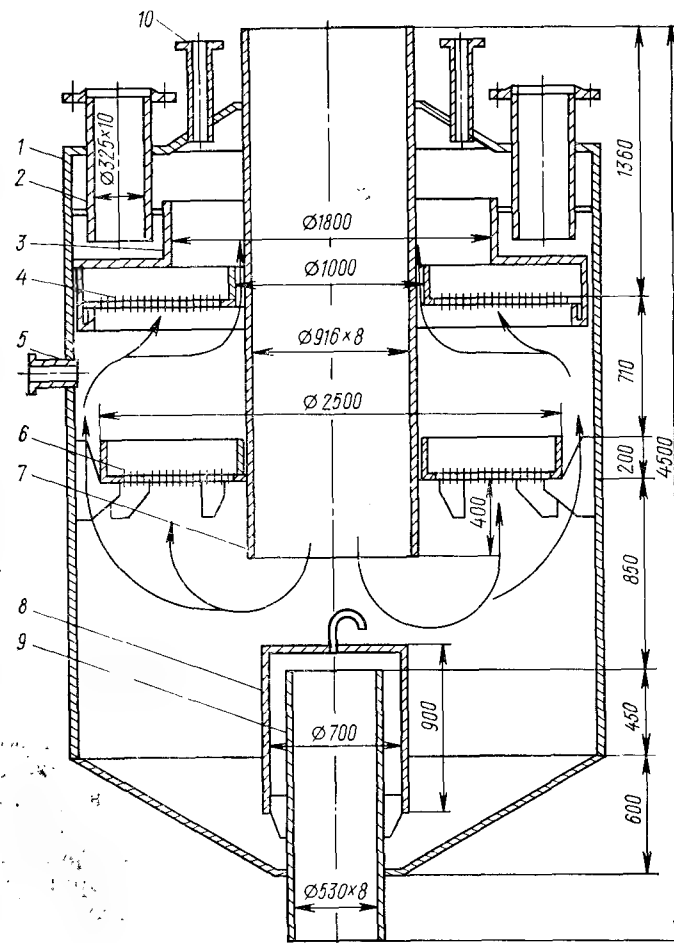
Регенеративный подогреватель смешивающего типа конструкции ЦКТИ.
